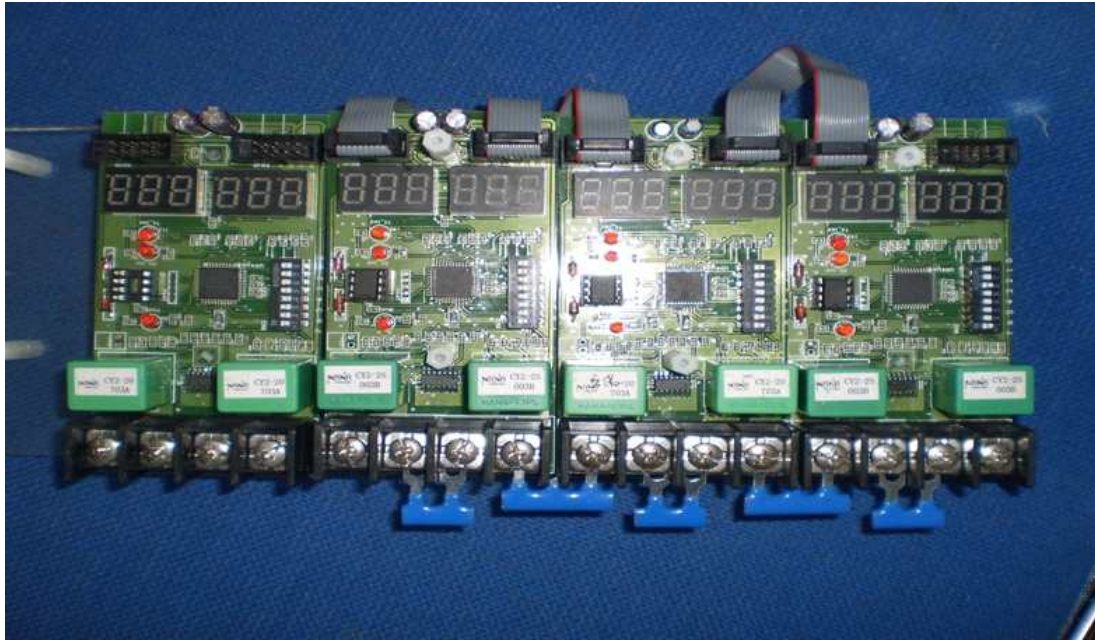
홀소자를 활용한 개도값 확인 장치 PCB
